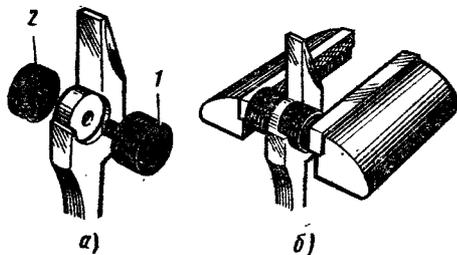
Шаблон-вкладыш для подгонки шарнирного соединения плоскогубцев: а — шаблон-вкладыш; б — установка и закрепление шаблона-вкладыша в тисках
